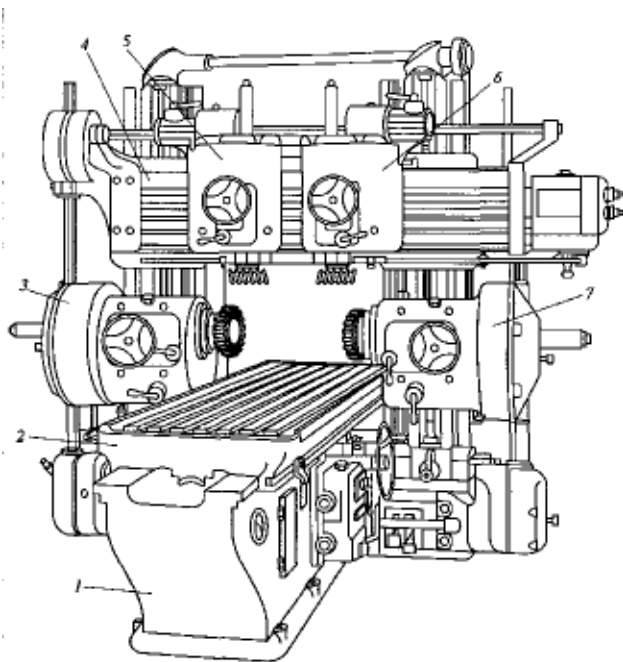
Загальний вигляд спеціалізованого фрезерного верстата
